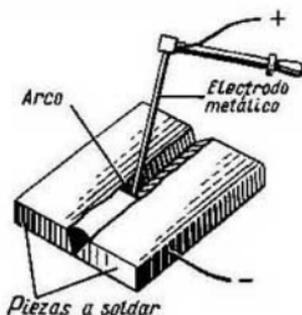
Soldadura eléctrica según el método de Slavianov (con electrodo metálico)
